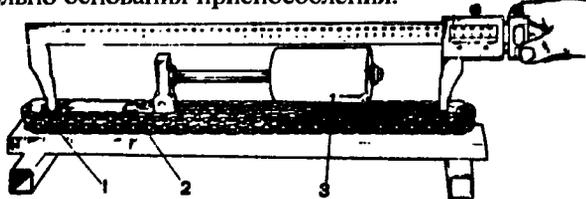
Приспособление 67.7824.9521 для проверки износа (вытяжки) цепи: 1 - ролик; 2 - регулировочная гайка; 3 - противовес
